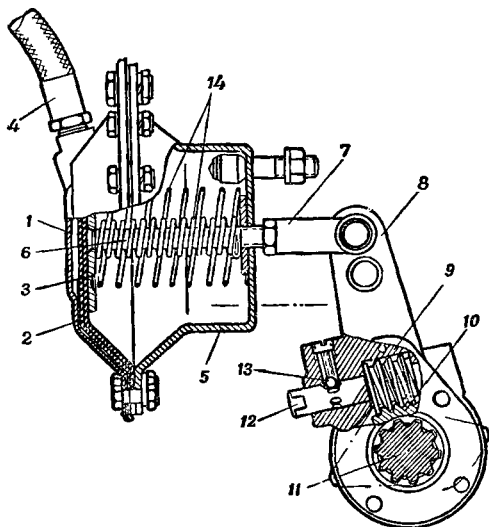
Рабочая тормозная камера пневматического привода тормозов автомобиля ЗИЛ-150.
